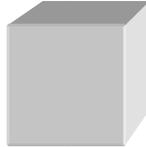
Diseño volumétrico de probeta con soldadura
